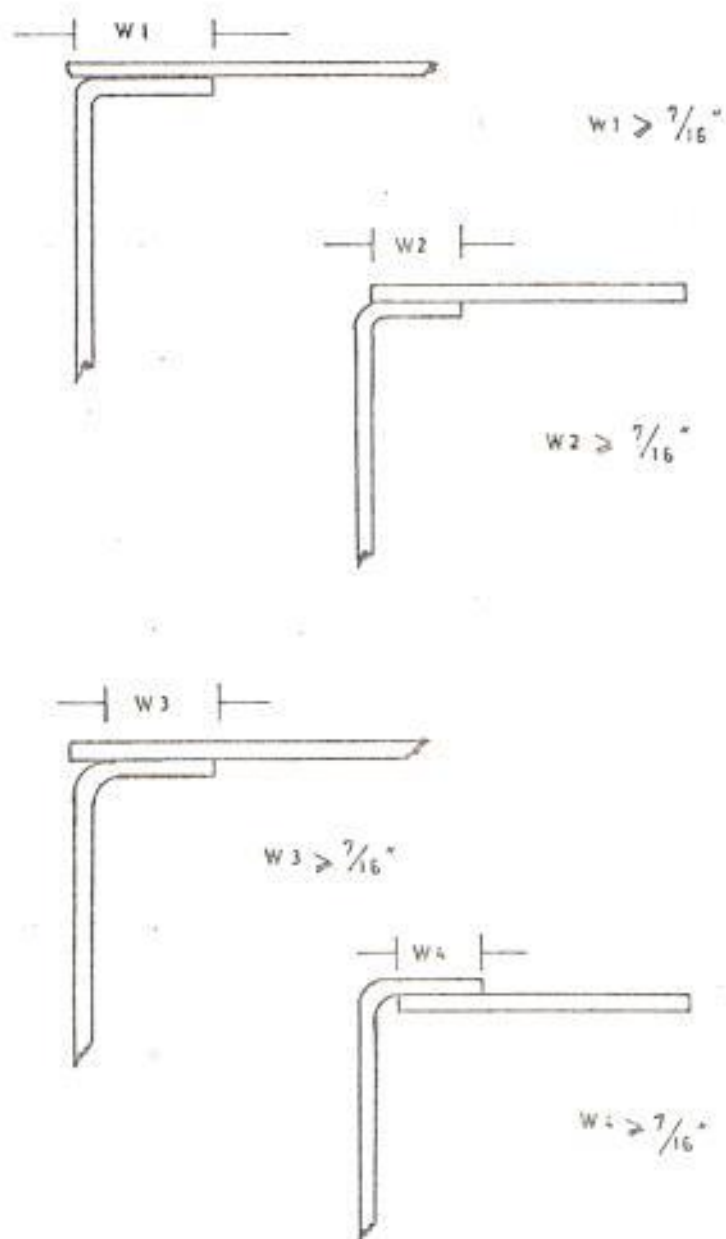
TRASLAPE ENTRE UNA CUBIERTA PLANA Y UN REBORDE DE UNA CAJA (ESQUINAS)
